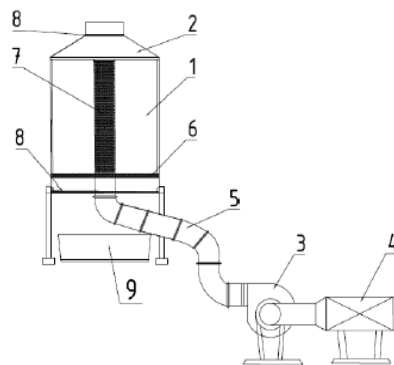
Конструкция камерной конвективной сушильной установки периодического действия. 1 – цилиндрический корпус; 2 – съемная крышка; 3 – вентилятор; 4 – калорифер; 5 – воздуховод; 6 – решетка; 7 – перфорированная труба; 8 – сито; 9 – поддон для сбора семян.
